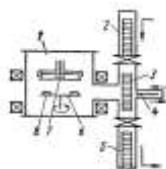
Установка непрерывного действия с закрытой шлюзовой системой
